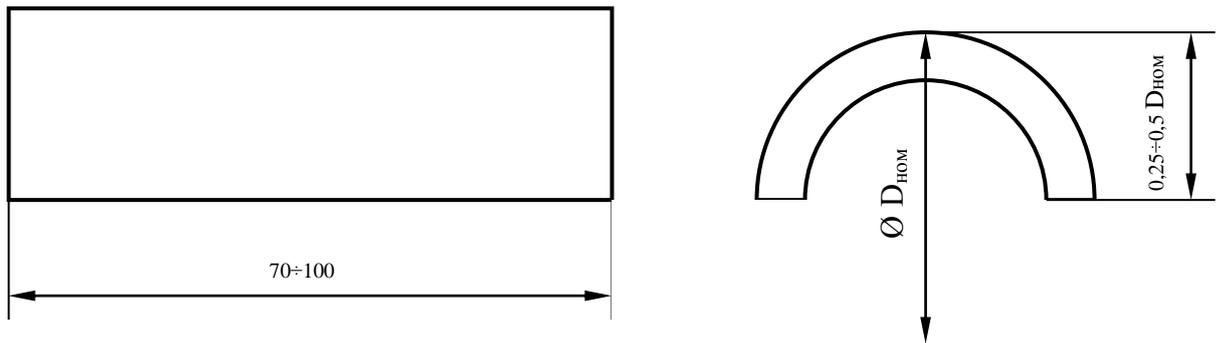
КО для настройки толщиномера при измерении толщины основного металла изделий с криволинейной поверхностью в виде труб: $D_{НОМ}$ – номинальный диаметр контролируемого элемента изделия
